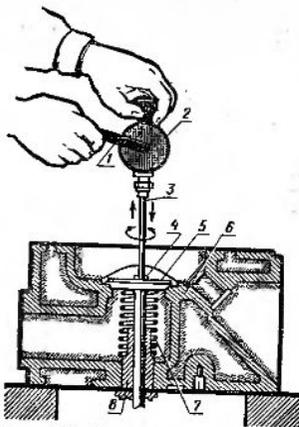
Прибор для притирки клапанов тракторного двигателя:
